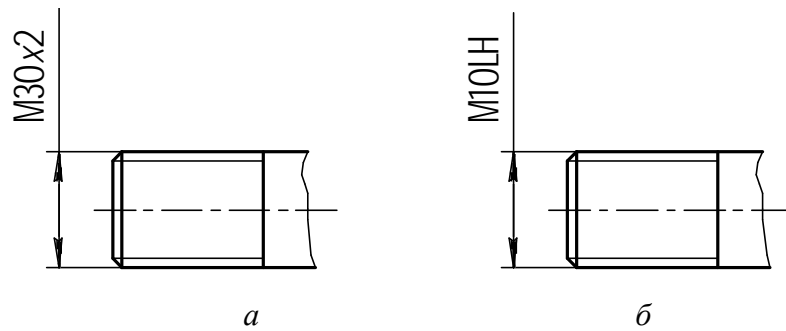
Нанесение размеров метрической резьбы на стержне
